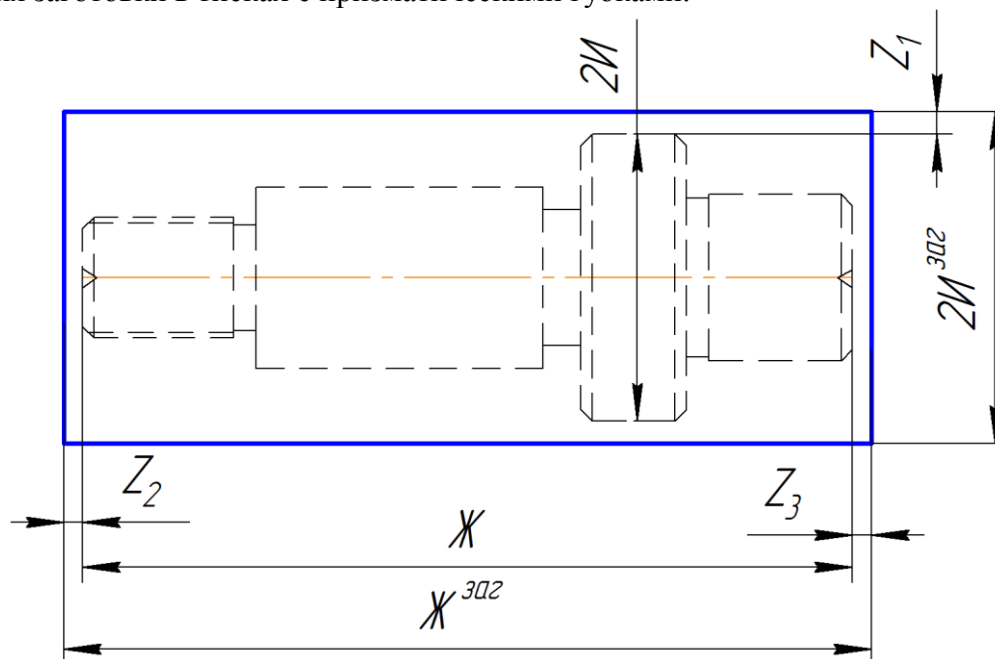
Теоретическая схема базирования заготовки детали «Валик»
